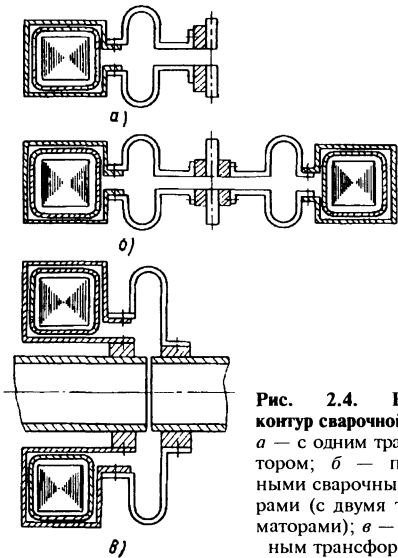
Вторичный контур сварочной машины: *a* — с одним трансформатором; *б* — параллельными сварочными контурами (с двумя трансформаторами); *в* — с контурным трансформатором
